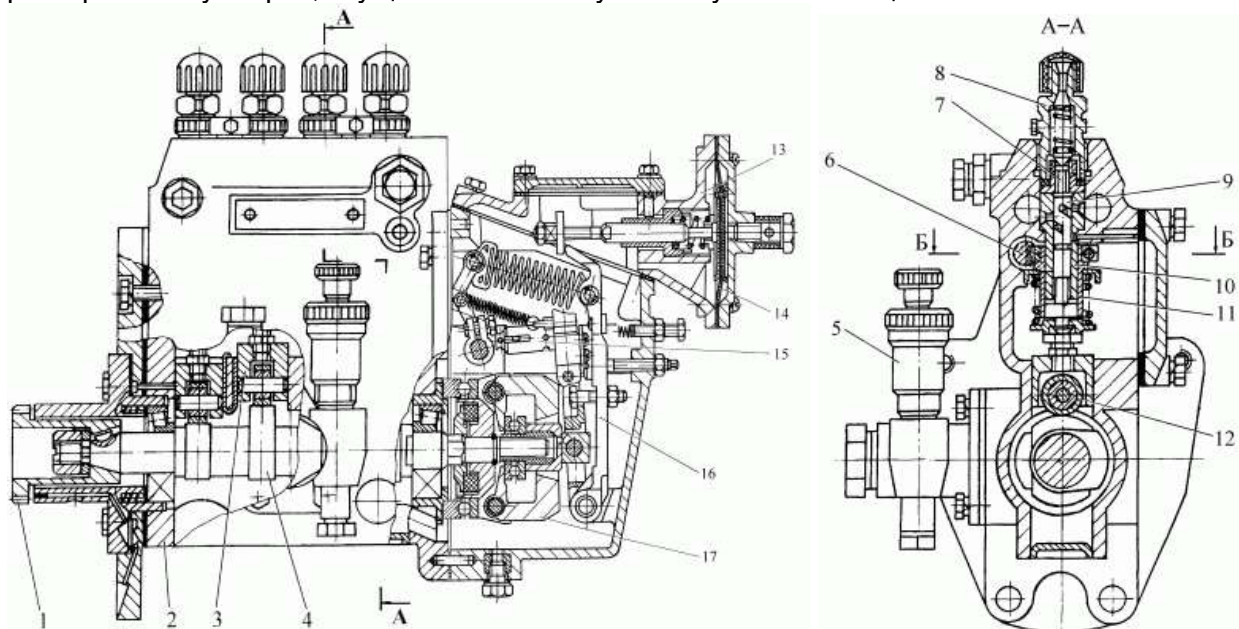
Топливный насос 4УТНМ-Т: 1 - шлицевая втулка; 2 - корпус ТНВД; 3 - толкатель; 4 - кулачковый вал; 5 - ТПН; 6 - рейка; 7 - нагнетательный клапан; 8 - штуцер; 9 - плунжер; 10 - втулка плунжера; 11 - поворотная втулка; 12 - ролик толкателя; 13 - корпус пневмокорректора; 14 - мембрана пневмокорректора; 15 - корректор; 16 - основной рычаг регулятора; 17 - груз.
